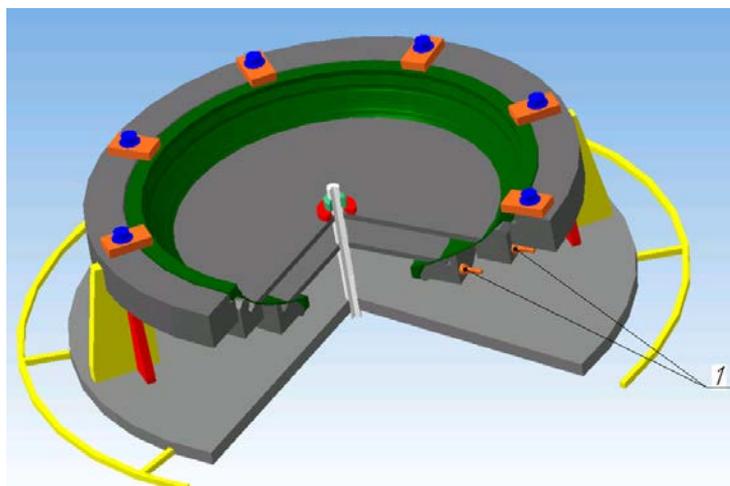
Сборочно-сварочная оснастка
